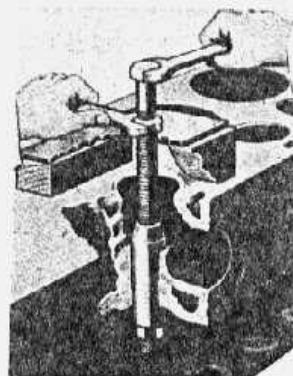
remoção das guias das válvulas de escapamento (motor de 6 cilindros)
